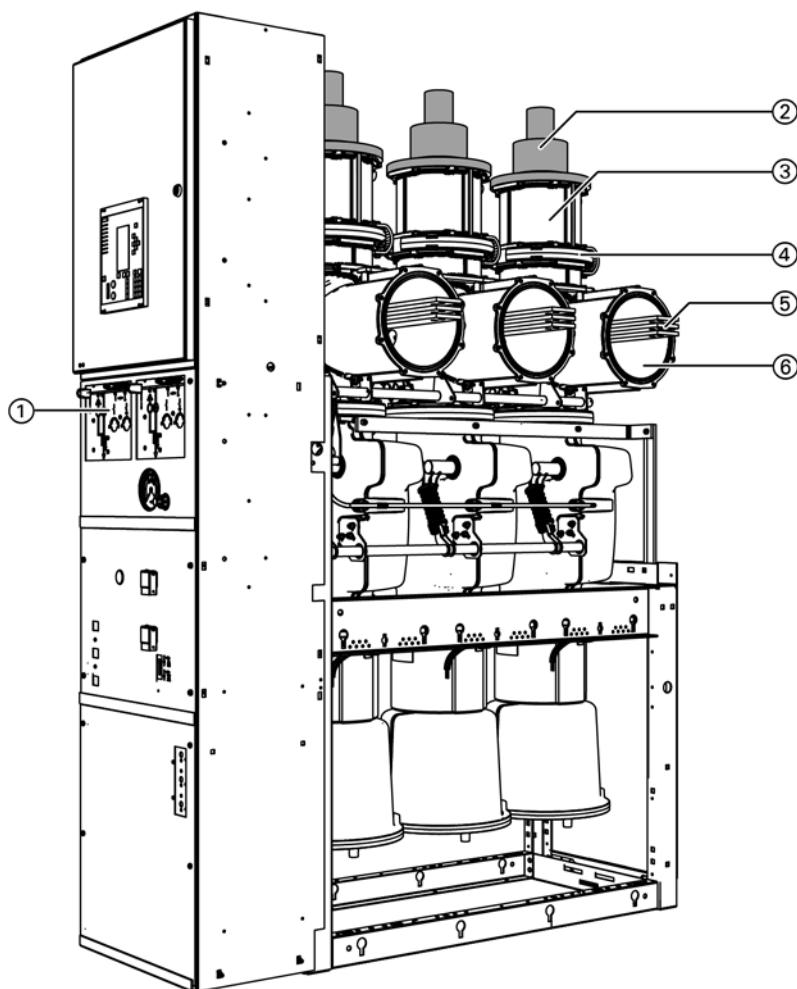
Обзор компоновки сборных шин: шина с элегазовой изоляцией с трехпозиционным разъединителем
